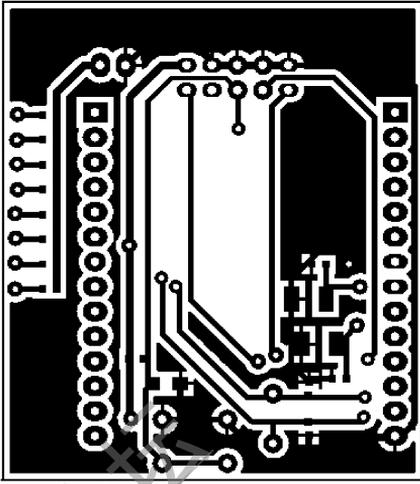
ATmega8 单片机 PACK 板电路和 PCB 图
